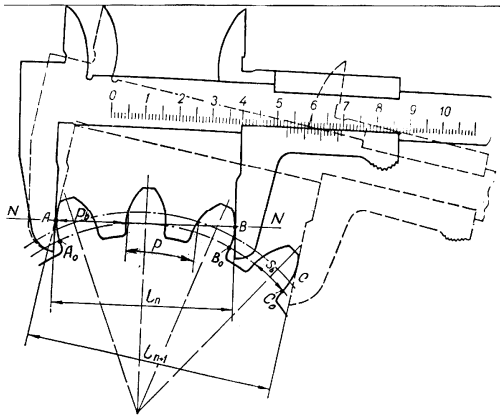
Схема вимірювання довжини спільної нормалі зубчастого колеса
